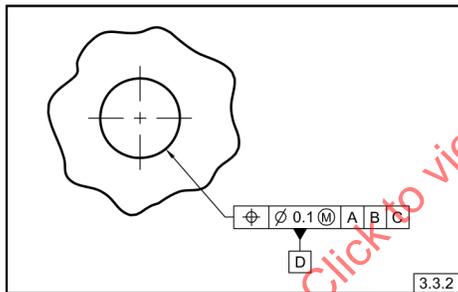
Ejemplos de Símbolos del Elemento Datum Objetivo
